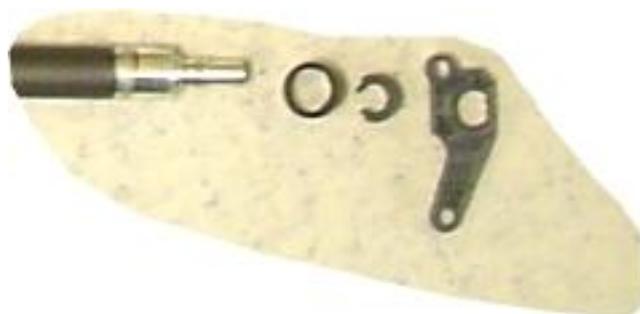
20 - Estabilizador do cilindro magnético - lado das engrenagens
